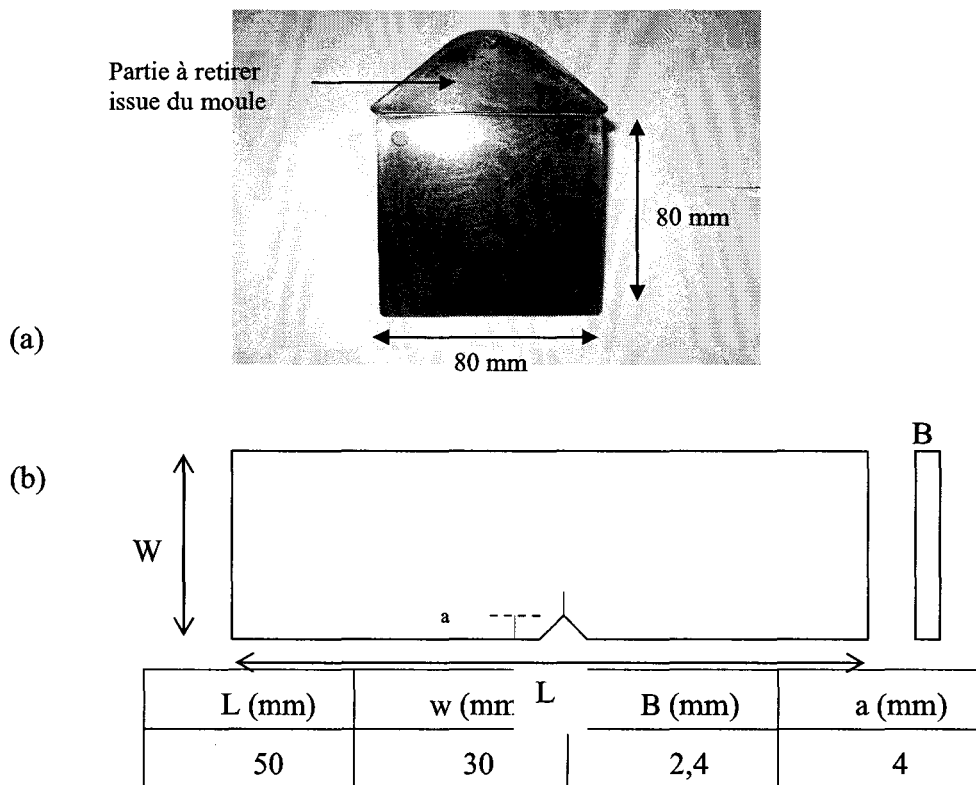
(a) plaques de polyamide obtenues par moulage par injection (b) Géométrie et dimensions en mm des éprouvettes SENT.
